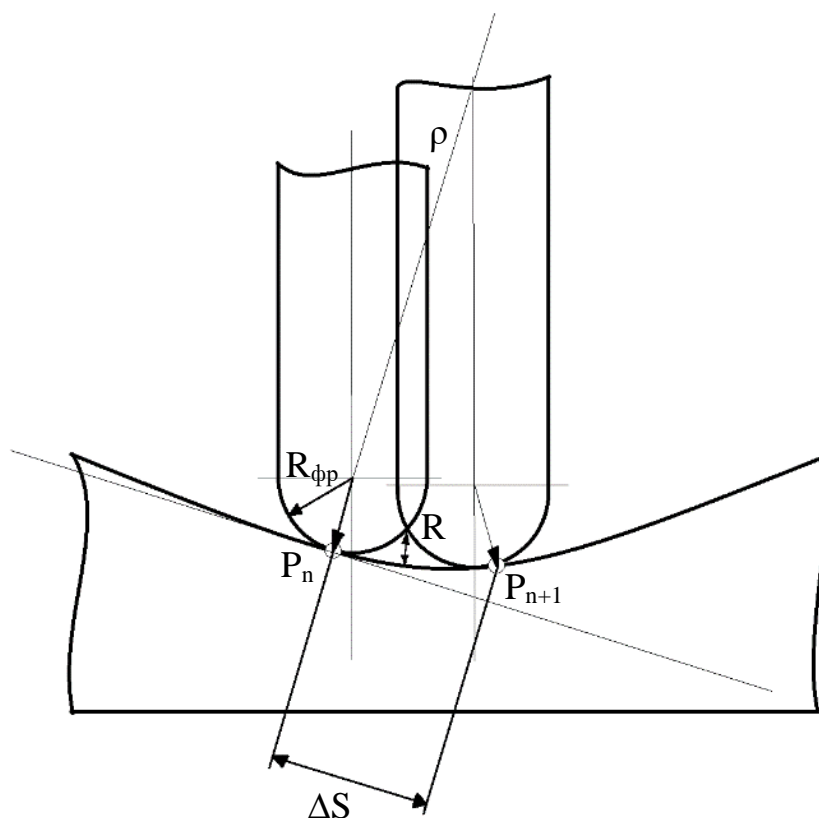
Схема формирования ребристости при фрезеровании формообразующей поверхности
